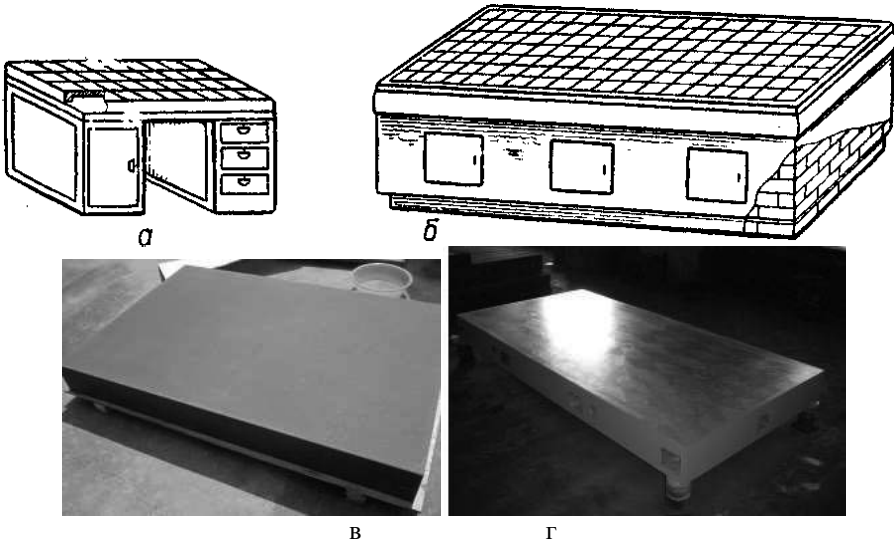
Розмічальні плити: а – чавунна на тумбі; б – чавунна на фундаменті; в – плита перевірна гранітна розмічальна 2000x1000; г – плита перевірно-розмічальна чавунна 2000x1000
